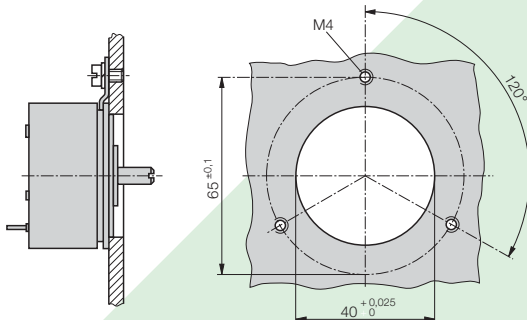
Bohrplan für Befestigung mit 3 Spannklammern.
